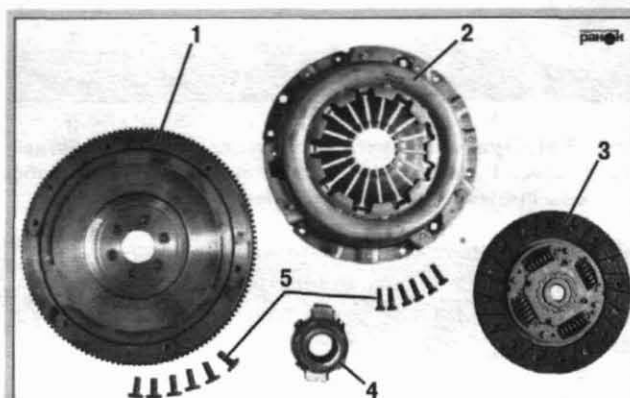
Детали сцепления: 1 – маховик; 2 – корзина сцепления; 3 – ведомый диск сцепления; 4 – выжимной подшипник; 5 – крепежные болты
